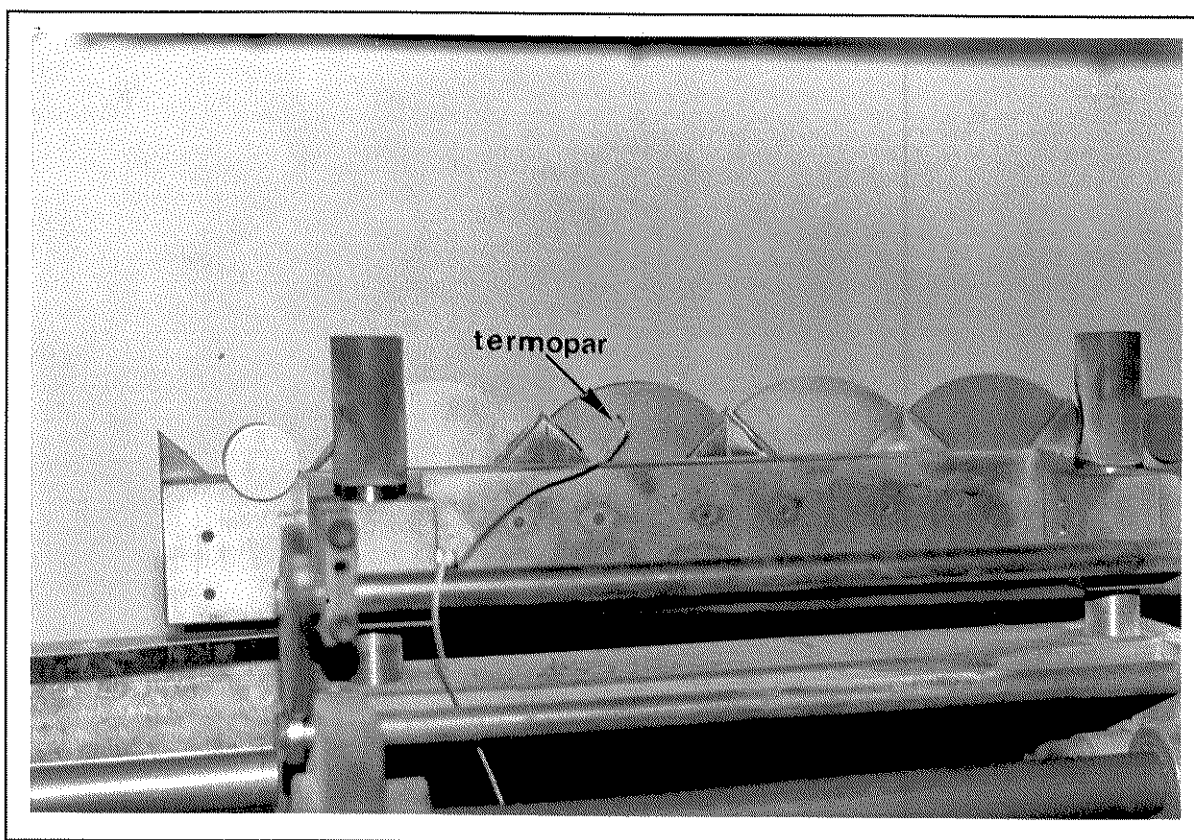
Termopar soldado no CP em disco.
